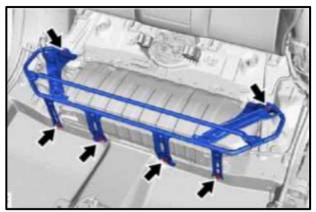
Desmontaje de estribo y cubiertas laterales Toyota
